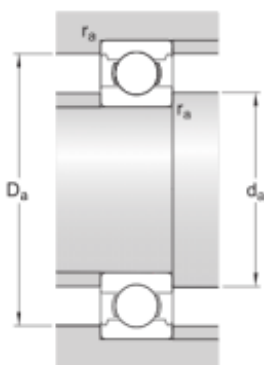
Ficha técnica del rodamiento rígido de bolas 608 – SKF
